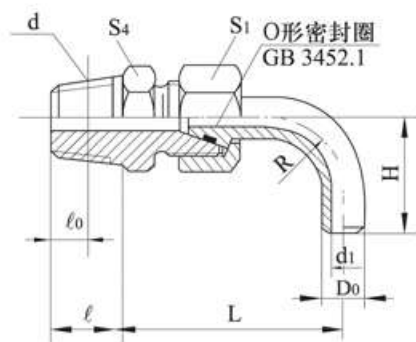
锥密封焊接式圆锥管螺纹90°弯管接头
